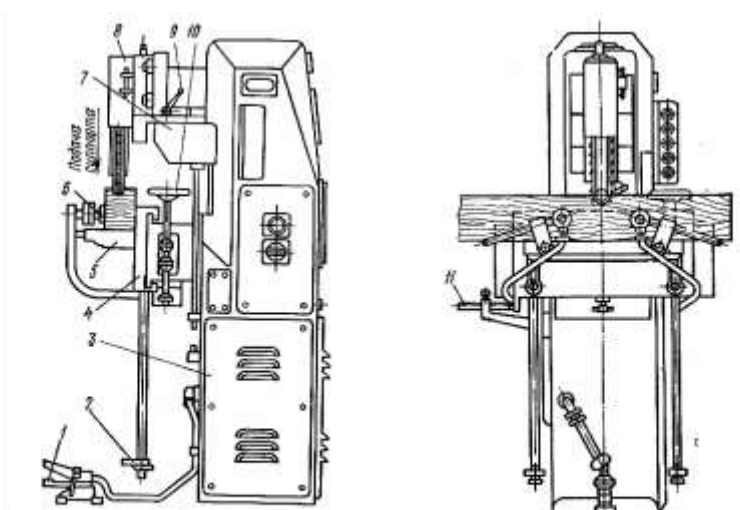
Цепнодолбежный универсальный станок ДЦА-4: 1 — педаль, 2 — упор, 3 — станина, 4 — вертикальная плита, 5 — горизонтальная плита, 6 — гидropriжим, 7 — суппорт, 8 — режущая головка, 9 — рукоятка, 10 — маховичок продольной подачи, 11 — ограничитель хода стола
